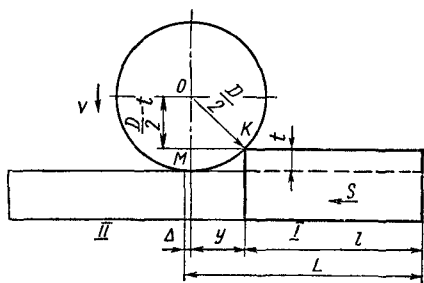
Элементы пути, проходимого заготовкой при цилиндрическом фрезеровании
